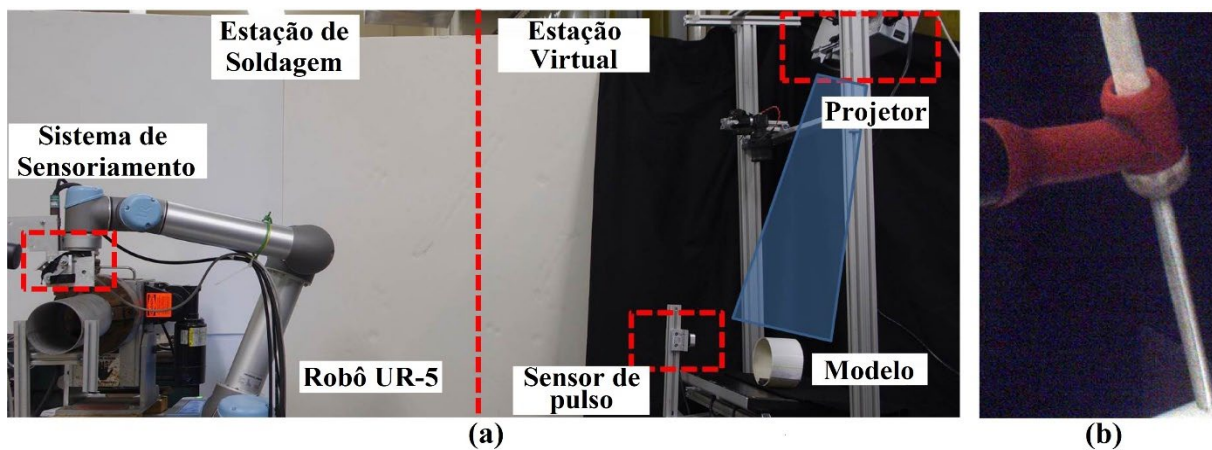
(a) Visão geral do sistema de soldagem virtual (b) tocha de soldagem virtual (com peso e tamanho similares à tocha de soldagem real) [117].
